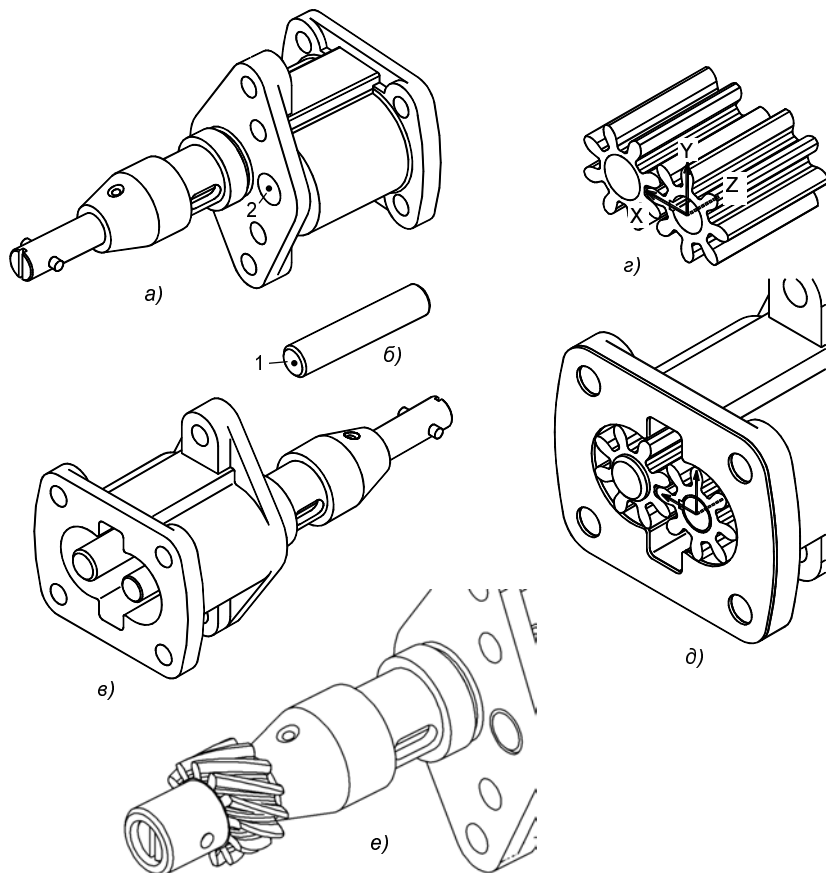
Установка штифта (а—в), цилиндрических зубчатых колес (г), создание прокладки (д), установка косозубой шестерни (е)
